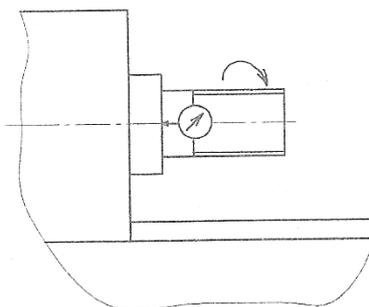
Схема установки индикатора для проверки радиального биения, центрирующей шейки шпинделя
